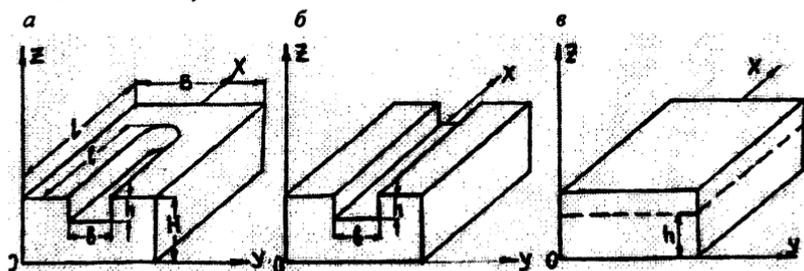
Виды обрабатываемых поверхностей и их расположение в системе координат
